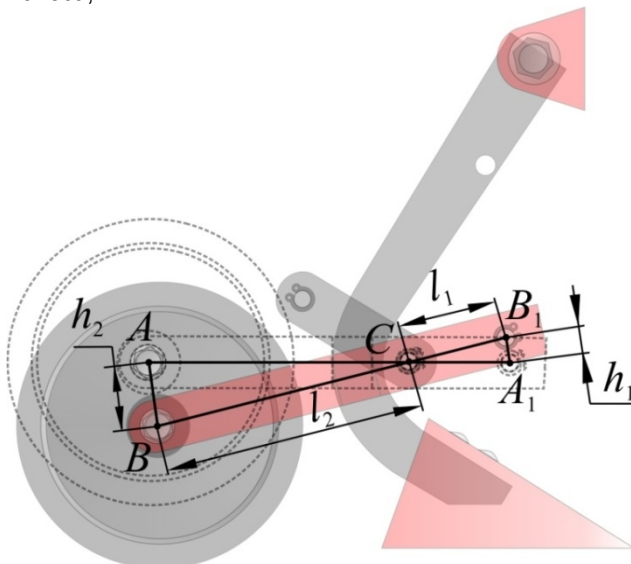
Схема перемещения прикатывающего бороздообразующего колеса
